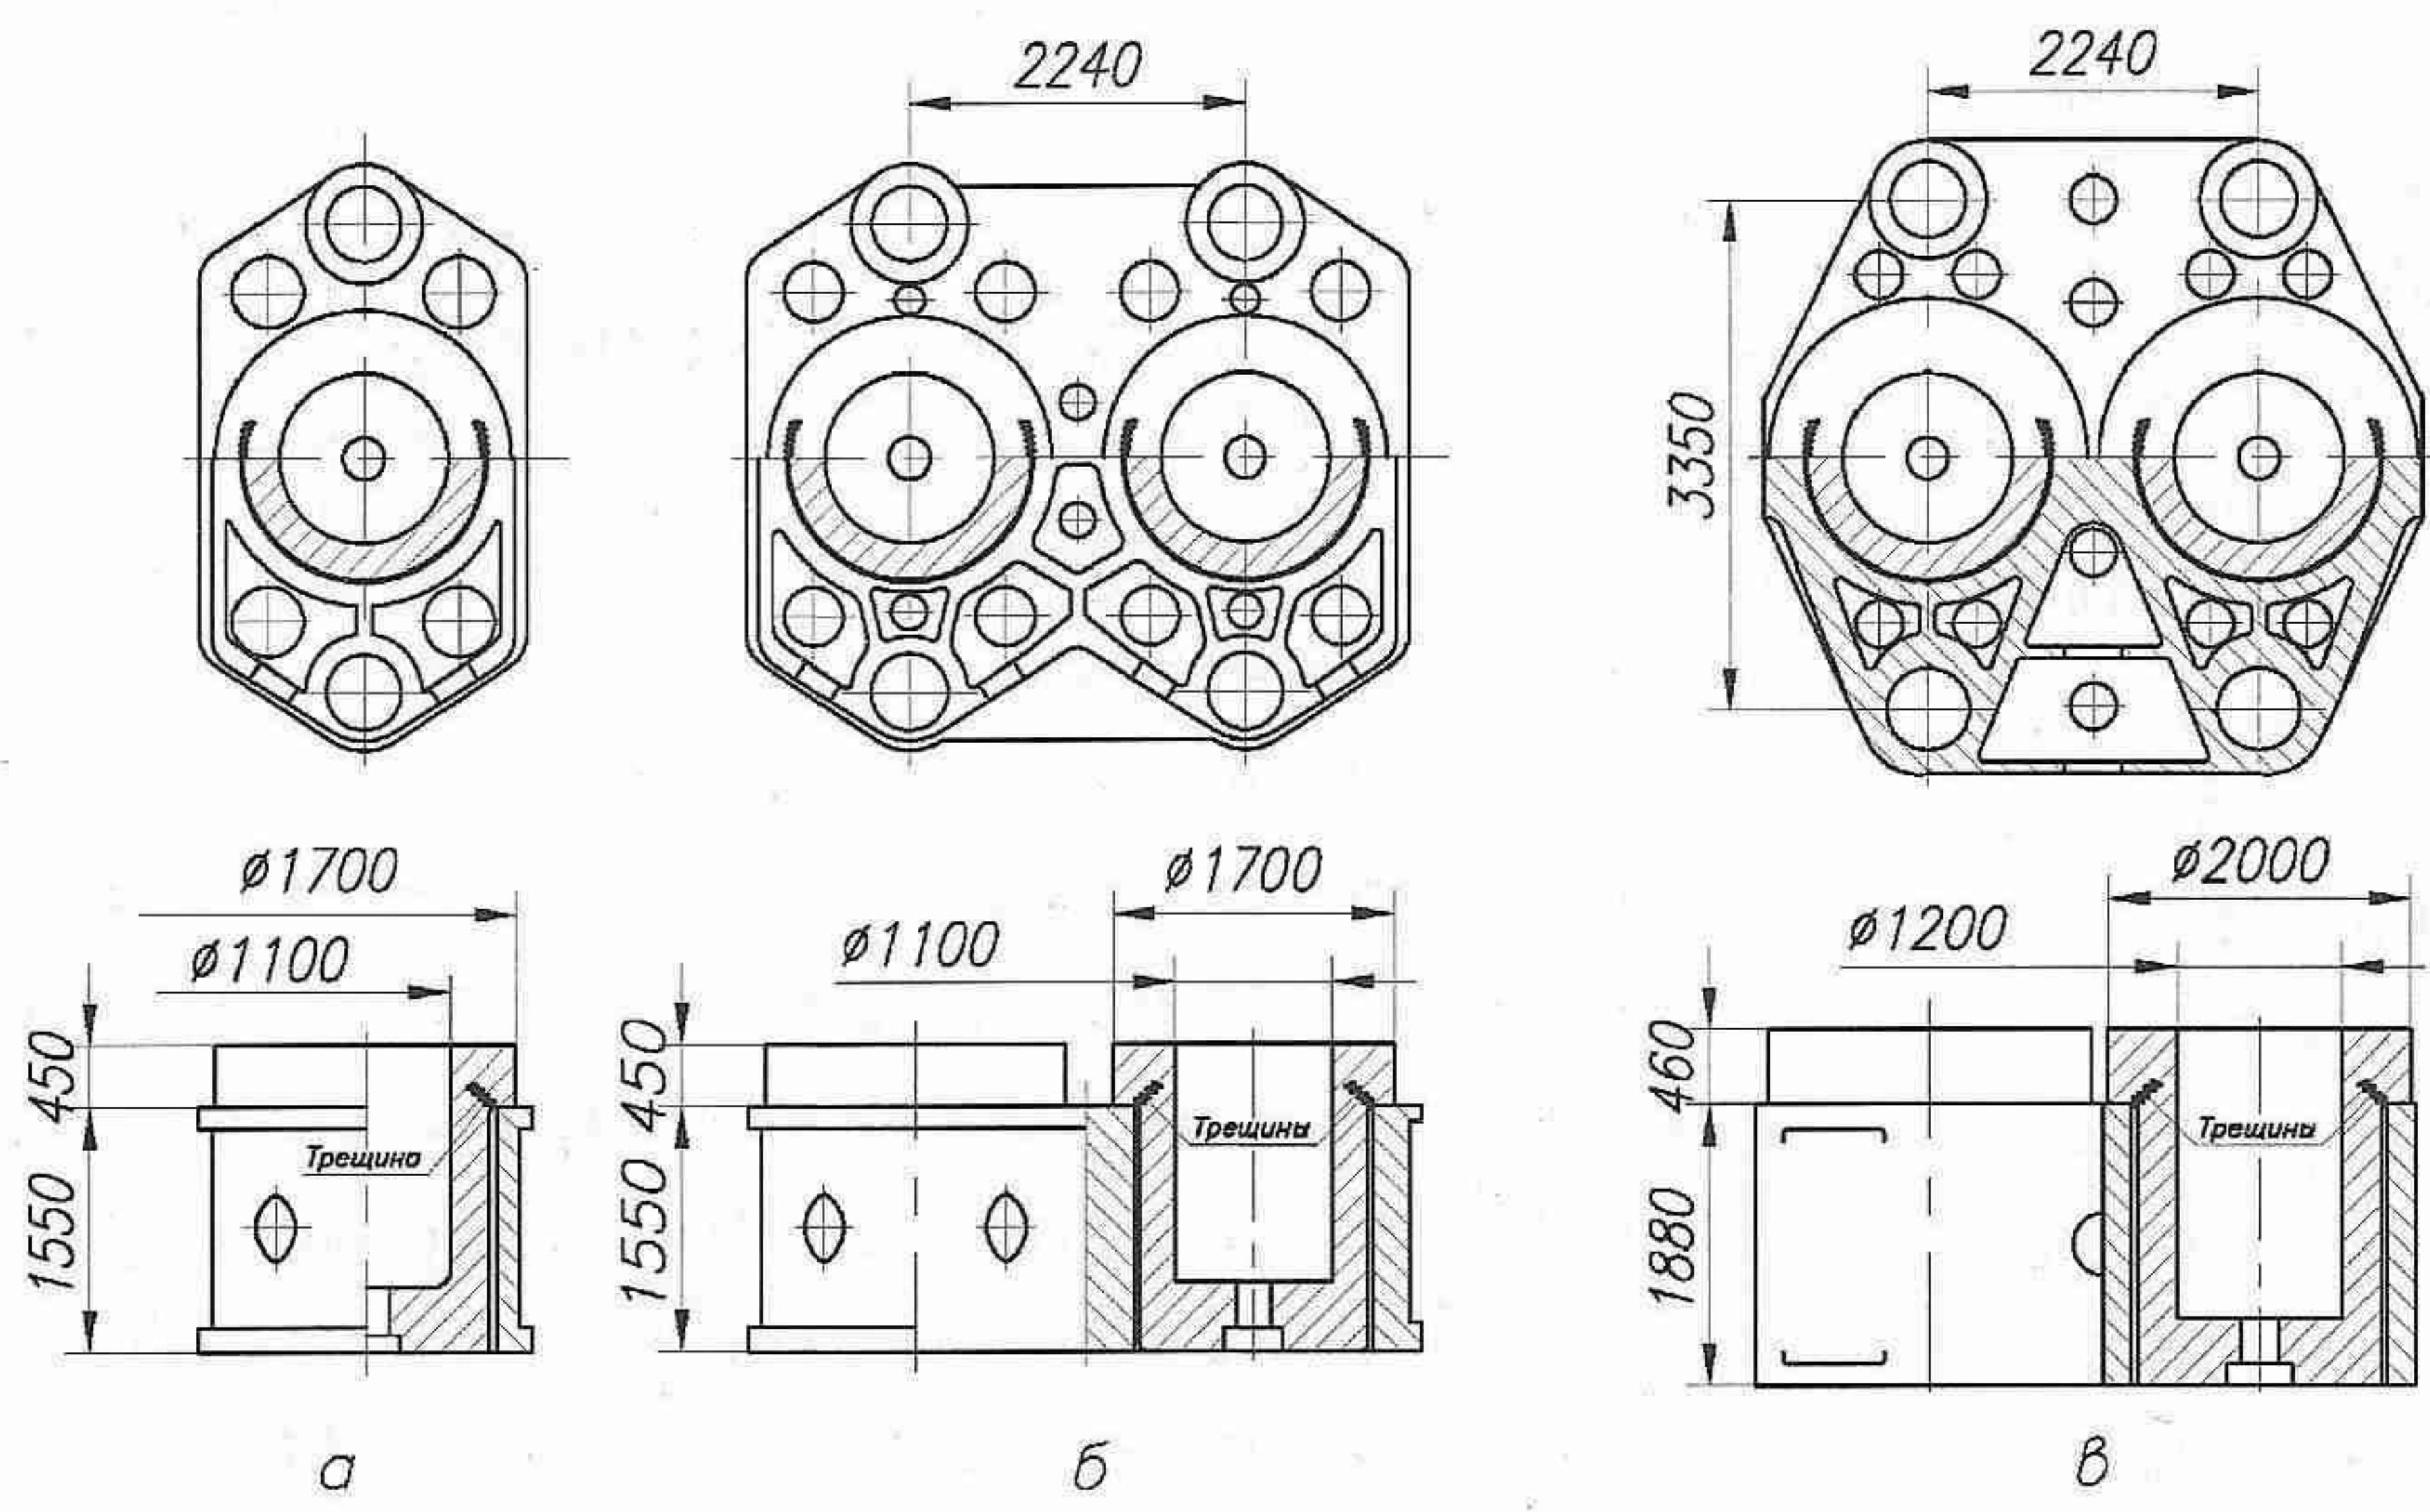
Разрушение цилиндров прессов силой 160 (а, б) и 200 (в) МН для формовки заготовок труб диаметром 1020...1220 мм (а, б, в — узлы поперечины)
